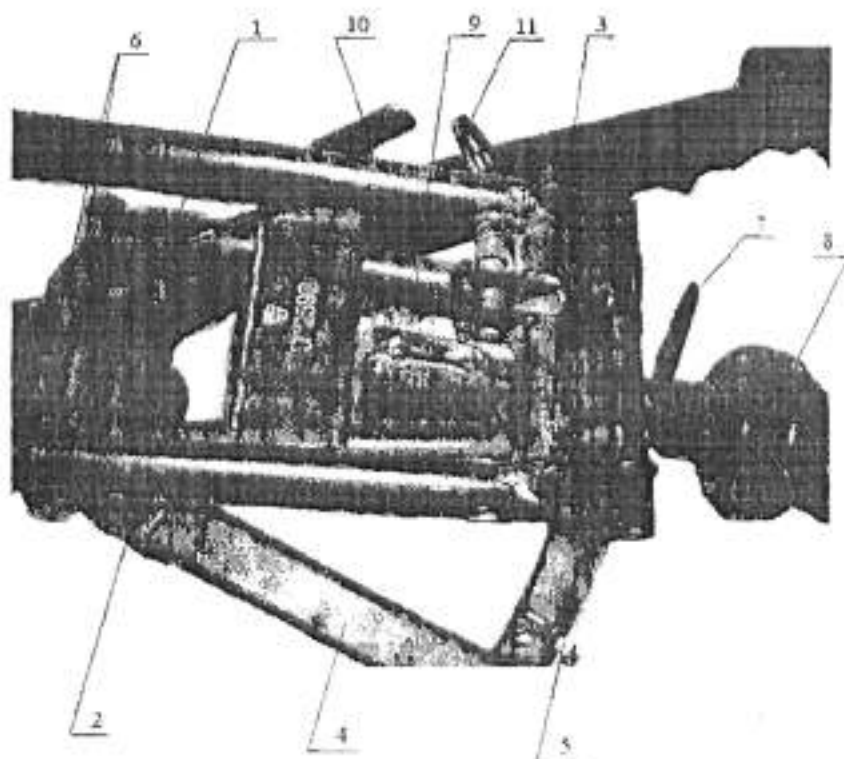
Верхняя и нижняя люлька станка Степанова под станковый гранатомет АГС-17 (Вид сверху)
